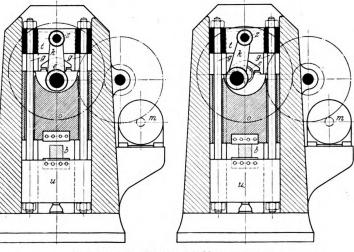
und 3. Schema der Messerführung. b Blockquerschnitt. e Exzenterwelle. g Stangen. k Kurbelstange. m Motor. o Obermesserschlitten. (Querbalken. u Untermesserschlitten. z Zapfen.
